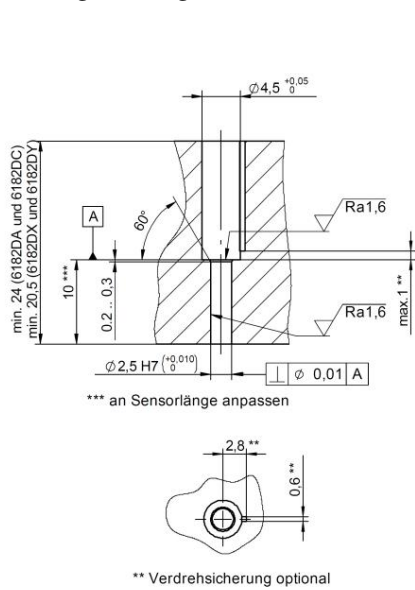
Montagebohrung für Einbau mit Distanzhülse
